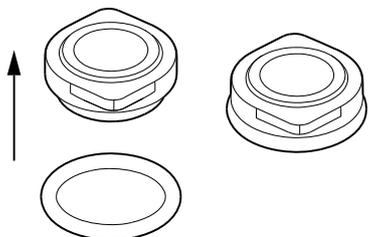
Монтаж уплотнительного кольца на неподвижной части торцевого уплотнения
